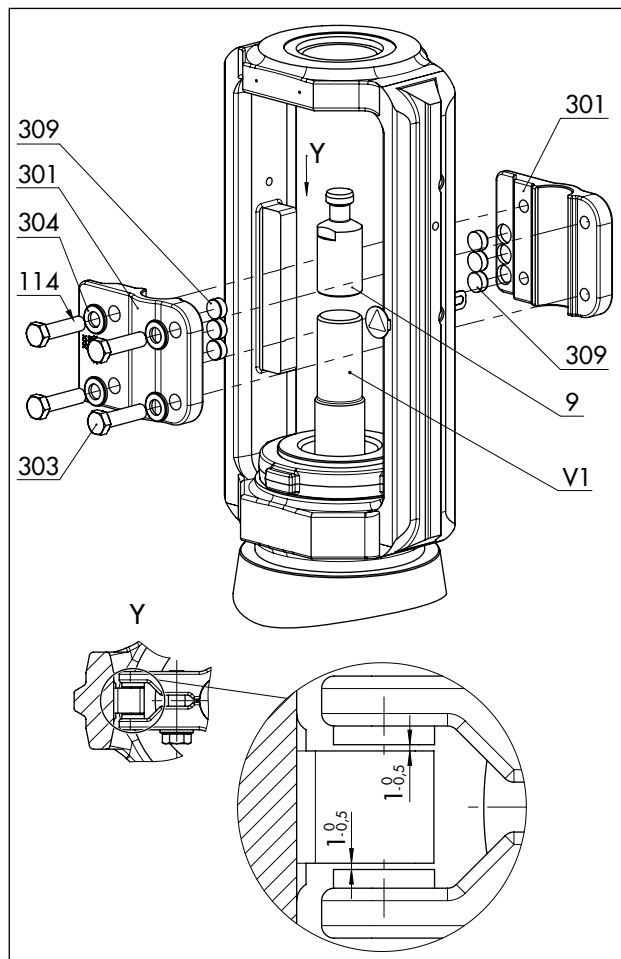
Montaje del seguro anti rotación en la ejecución estándar
